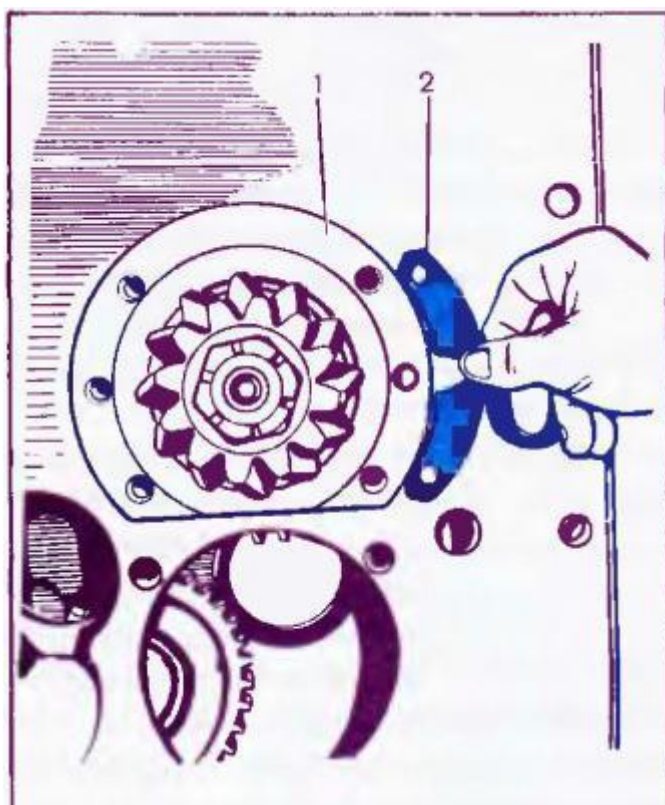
Регулировка осевого зазора трактора МТЗ в подшипниках вторичного вала
